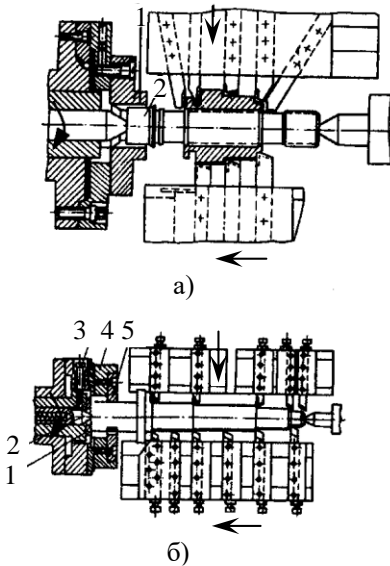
Схеми налагодок багаторізевого верстата для обточування:
